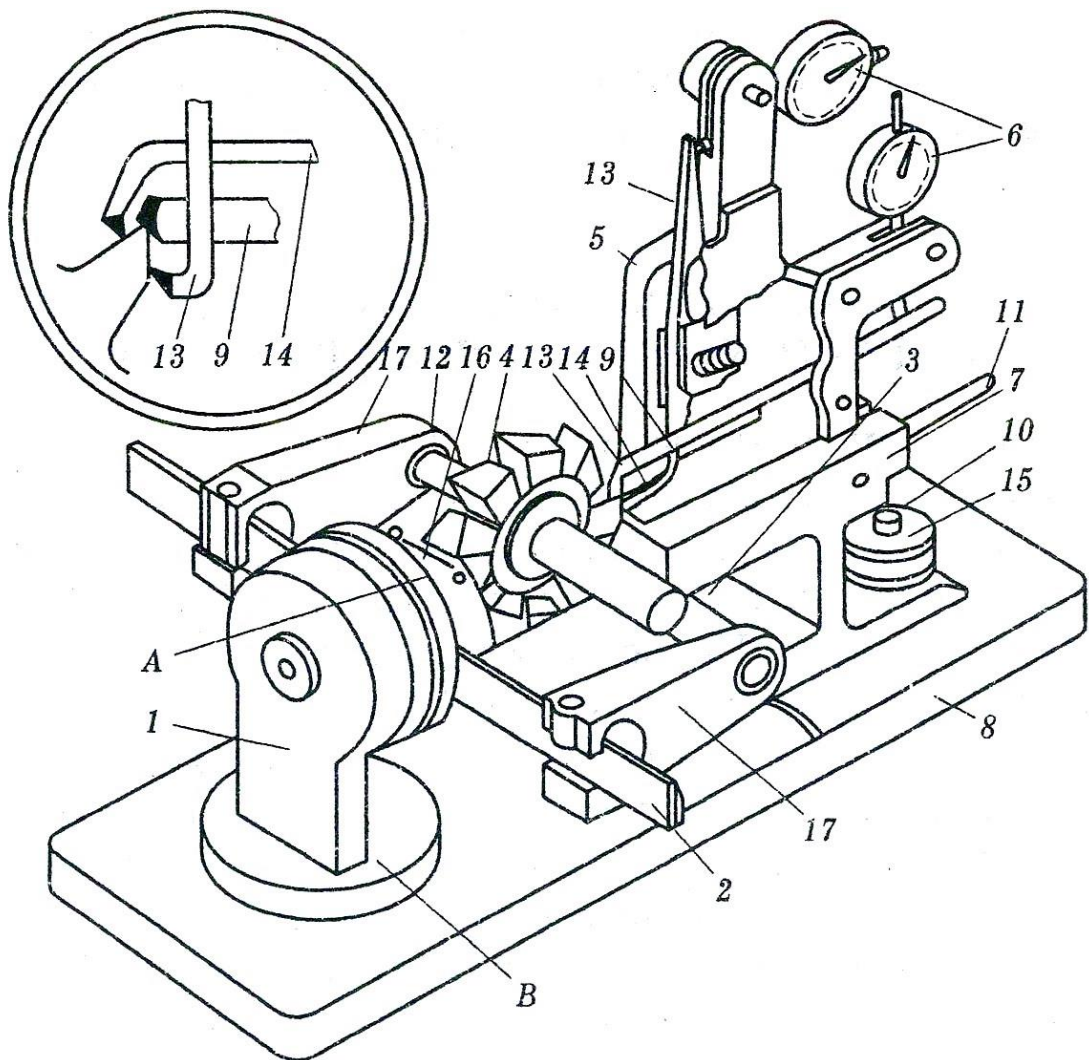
Индикаторный прибор для контроля углов заточки многолезвийных инструментов: 1 - корпус; 2 - линейка; 3 и 4 - центры; 5 - мерительная головка; 6 - индикаторы; 7 - основание; 8 - плиты; 9 - упор; 10 - винт; 11 - рукоятка; 12 - эталон; 13 и 14 - рычаги; 15 - гайка; 16 - поворотная планшайба; 17 - кронштейн
